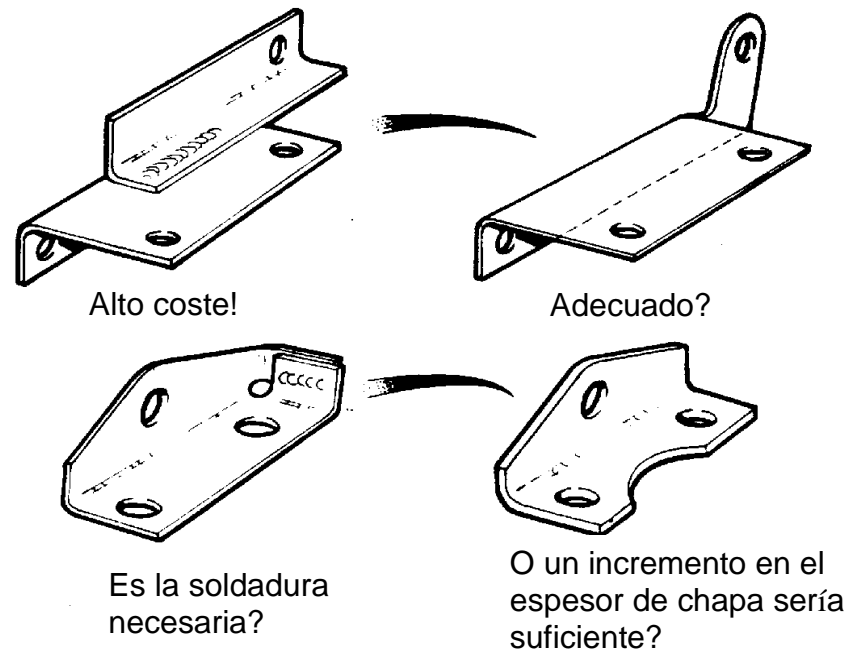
Evitar soldaduras mediante otros cambios en el diseño
